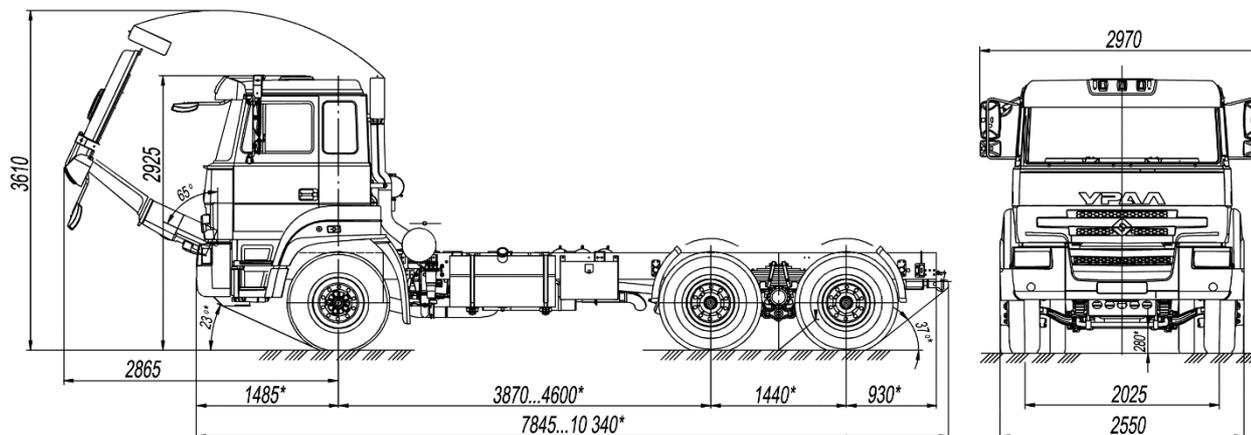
Габаритные размеры шасси Урал- С34520
